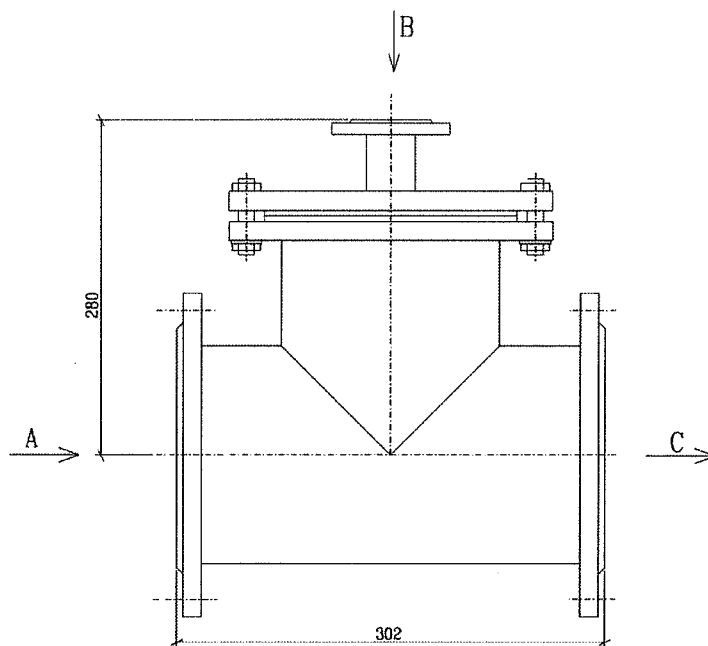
Габаритный чертеж смесителя для приготовления регенерационных растворов кислоты LDP30AM001
